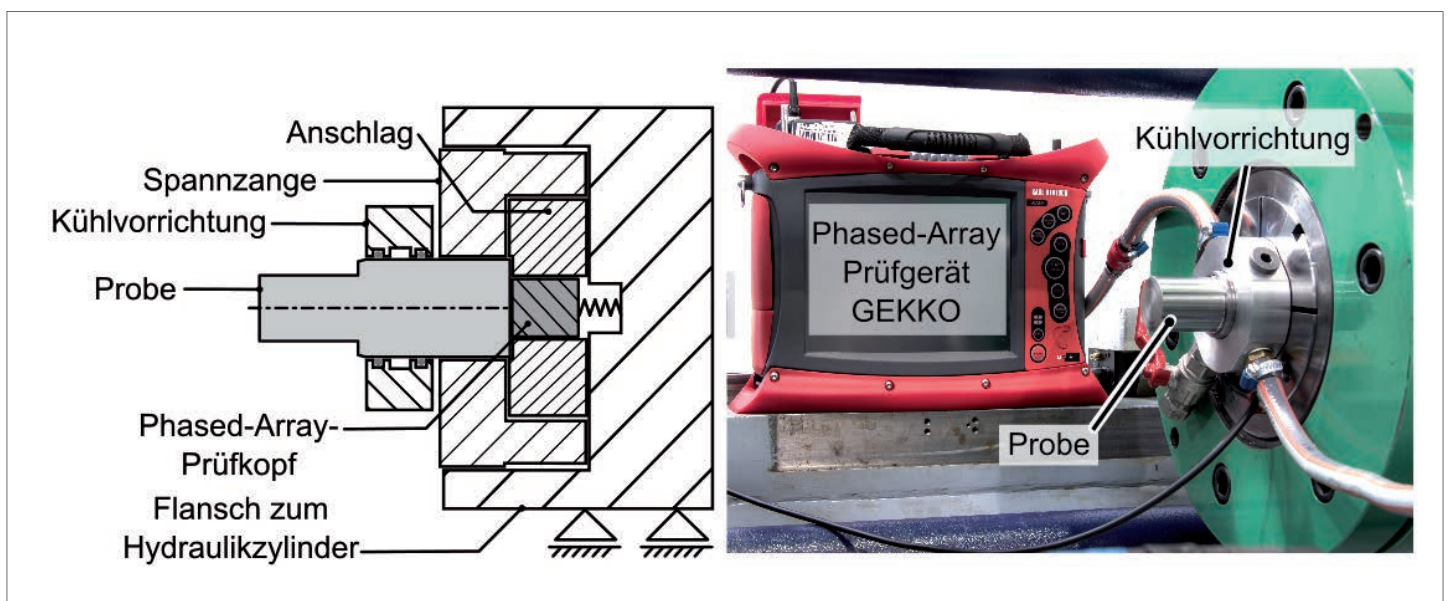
Skizze und Photo zeigen den Versuchsaufbau mit dem feststehend eingespannten Teil der Probe vor dem Schweißvorgang
